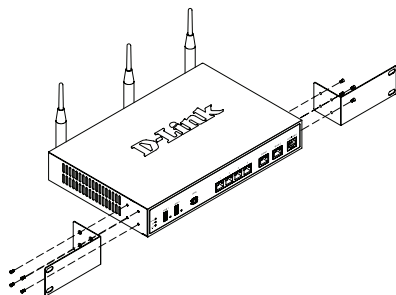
Instalação dos Suportes de Montagem do Bastidor
